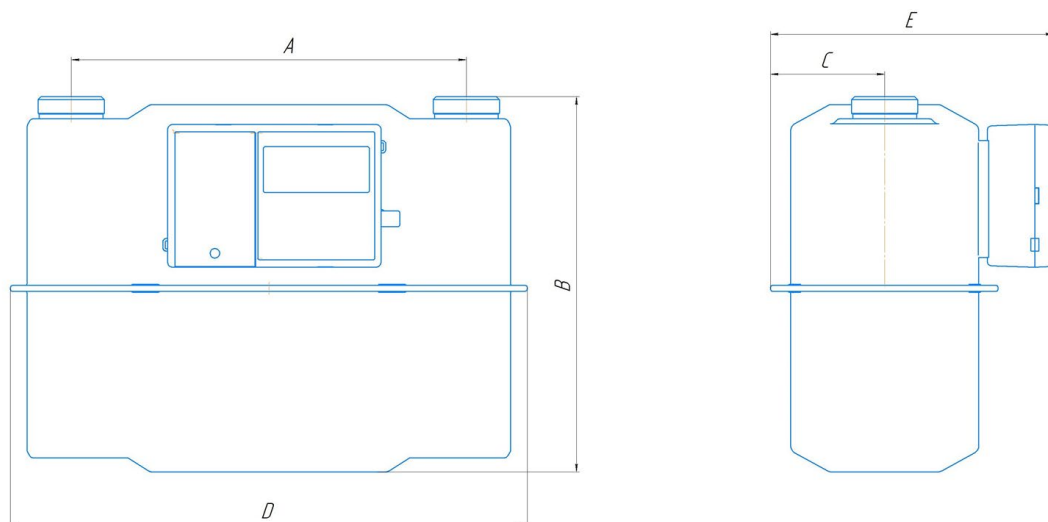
Габаритные и присоединительные размеры счетчиков типоразмеров G1,6-G25 в исполнении 1
